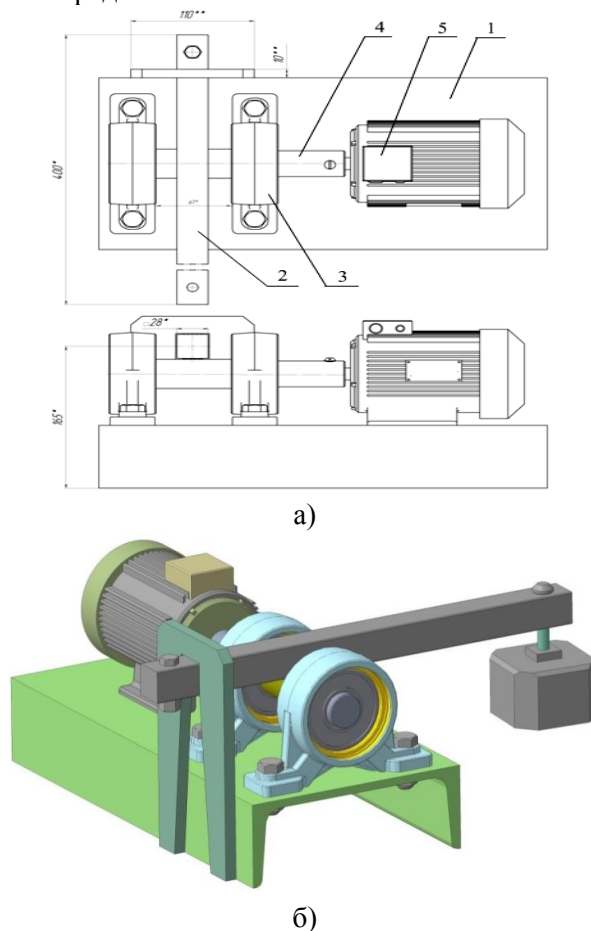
Установка для діагностування підшипників кочення: а) схема установки; б) тривимірний модель установки; 1 – рама; 2 – навантажувальний механізм; 3 – опора підшипника; 4 – проміжний вал; 5 – електродвигун
